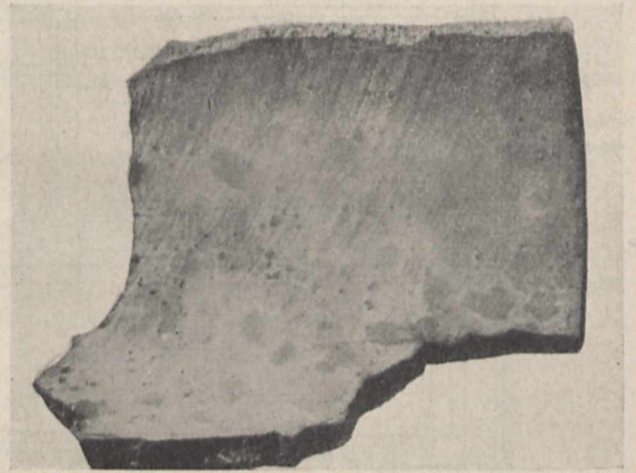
Kalk-Rostschuttschicht auf Gußrohrstücken
